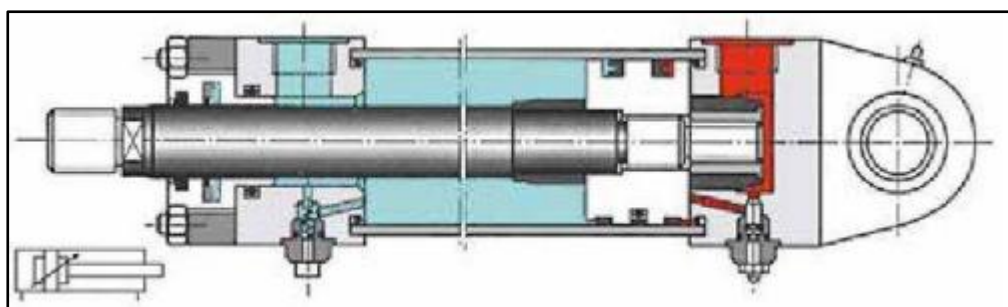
Cilindro de ação dupla com tirantes e fixação por flange na tampa dianteira
